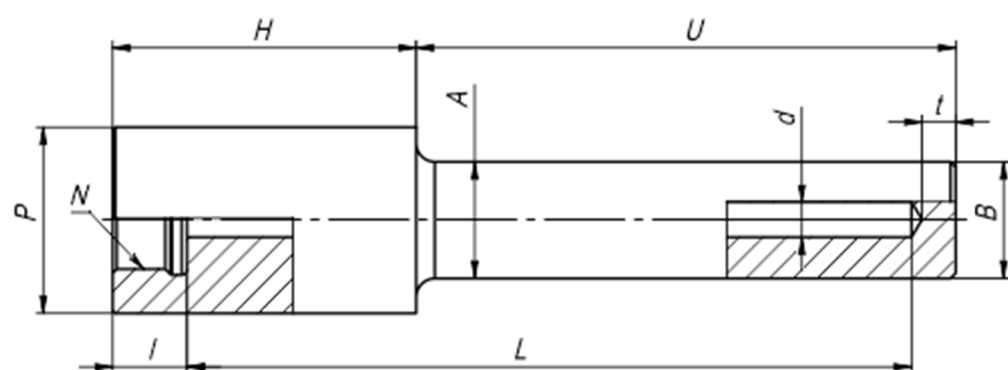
Гильза под приварку через адаптер (Socket Weld), цельноточёная, прямая, под подвижный штучер.
